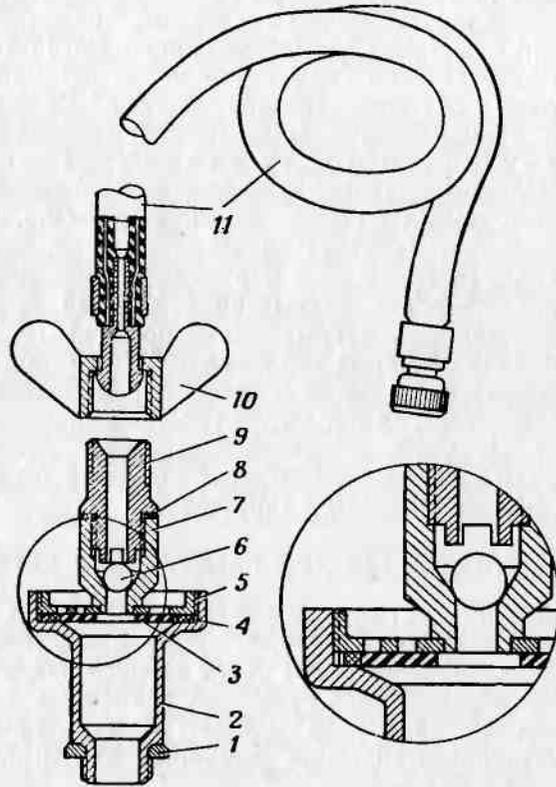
Приспособление для накачивания шин: 1 — прокладка; 2 — корпус приспособления; 3 — впускной клапан; 4 — прокладка; 5 — крышка; 6 — шарик выпускного клапана; 7 — корпус выпускного клапана; 8 — прокладка; 9 — штуцер; 10 — гайка-барашек шланга; 11 — резиновый шланг
